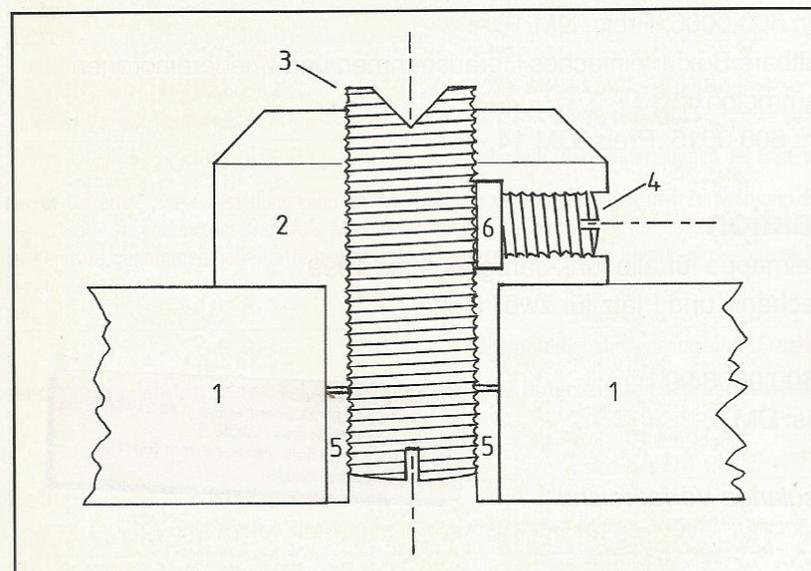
Das untere Spitzenlager: 1 Grundplatte, 2 unterer Lagerbock, 3 Lagerpfanne in FG-Schraube, 4 Halteschraube, 5 Makrolon-Zylinder, 6 Makrolon-Klötzchen.
